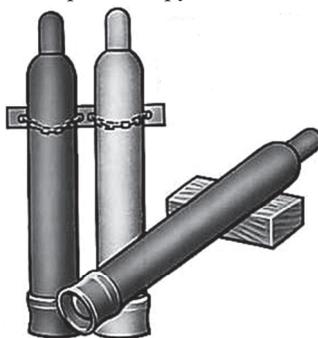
Положение баллона на месте производства газовой сварки
